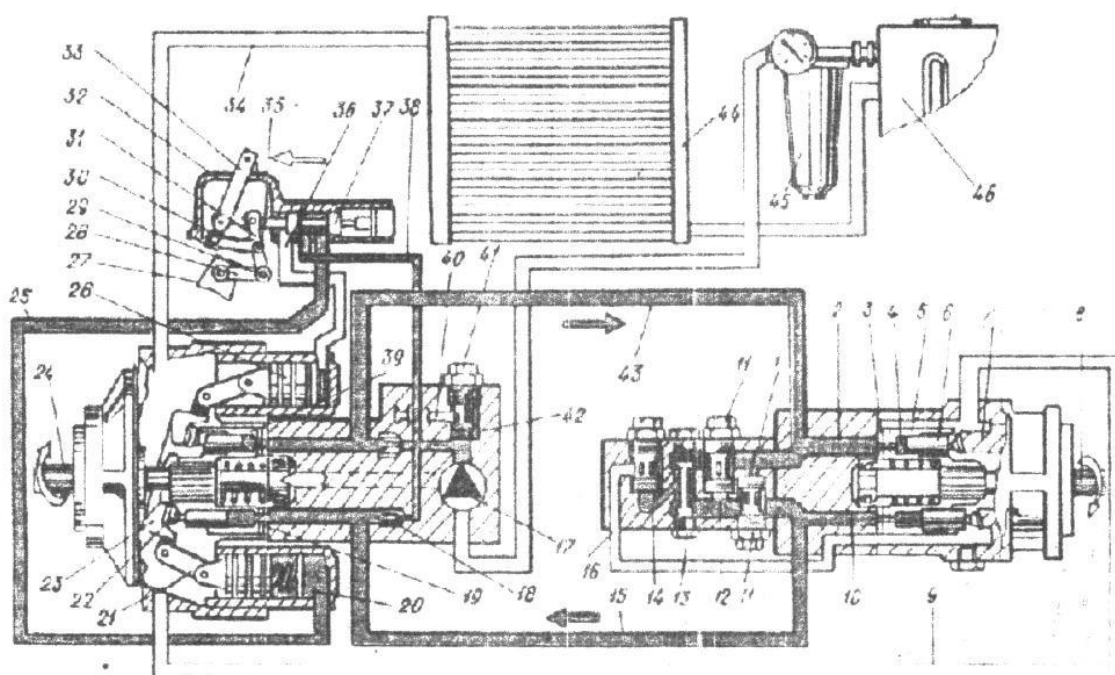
Схема работы ГСТ- движение вперед: 1,2,10,12,16,25,36,40- каналы подачи масла; 3, 19- запорнораспределительное устройство; 4- рабочая камера; 5, 39- блок цилиндров; плунжер; 7- наклонная шайба; 8, 24- валы; 9,15, 34,43 - гидролинии; 11 - клапаны высокого давления; 13- золотник; 14- переливной клапан; 17 - насос подпитки; 18, 42 - обратные клапана; 20, 26 сервоцилиндры; 21 - серьга; 22- подпятник; 23 - люлька; 27, 31, 33 - рычаги; 28,30 - тяги; 29, 35 - оси; 32 - корпус распределителя; 37 - золотник; 41 - предохранительный клапан; 44 - масляный радиатор; 45 - фильтр; 46 - масляный резервуар.
